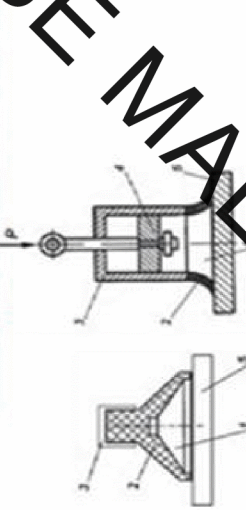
Пасивні вакуумні пристрої з корпусом з еластичного матеріалу
